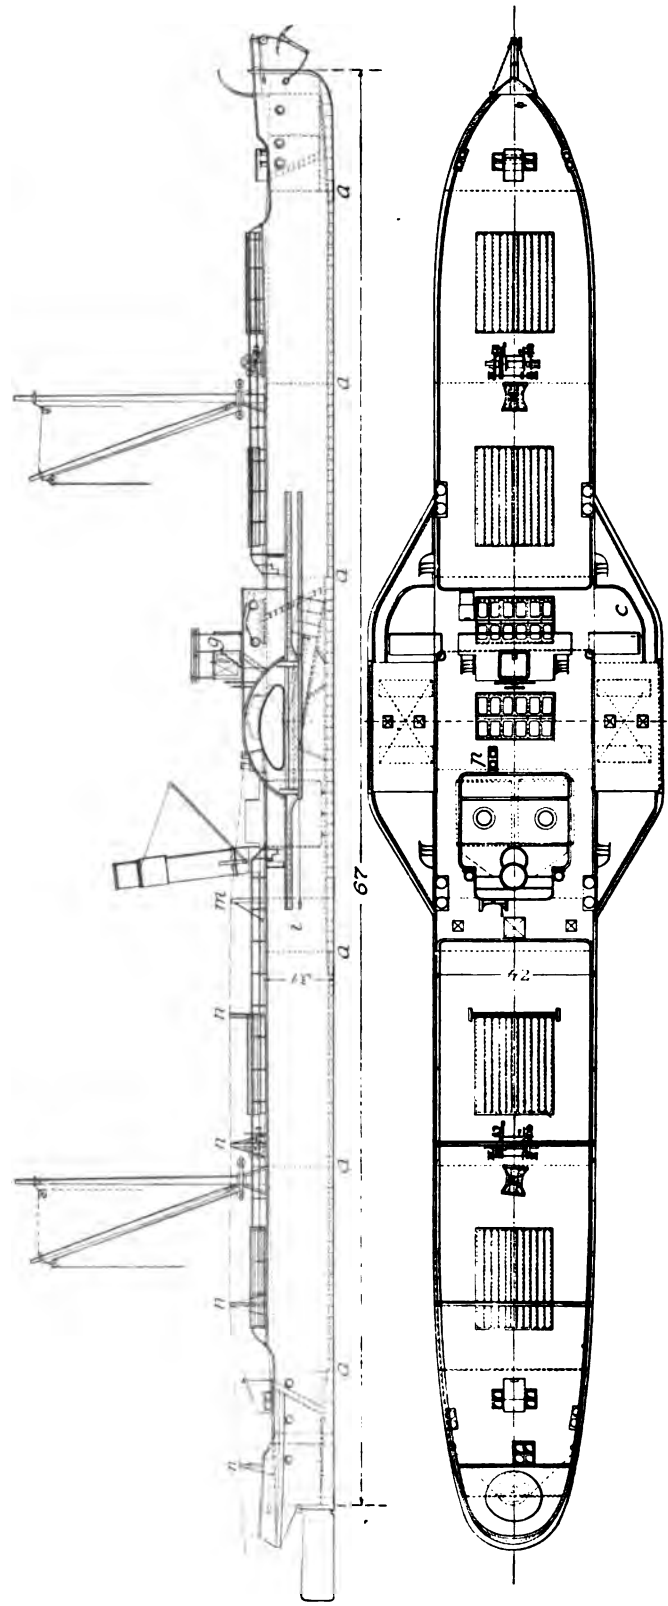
und 472. Güterdampfer mit Seitenrädern und 400 PSi auf der Elbe 1 : 350.
